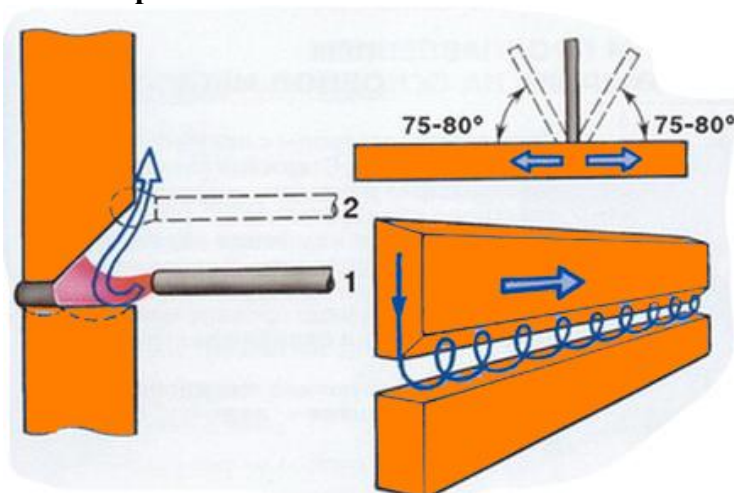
Тип шва – С8, сварка ручная дуговая ГОСТ 5264-80, положение шва – вертикальное; толщина металла – 10 мм.
